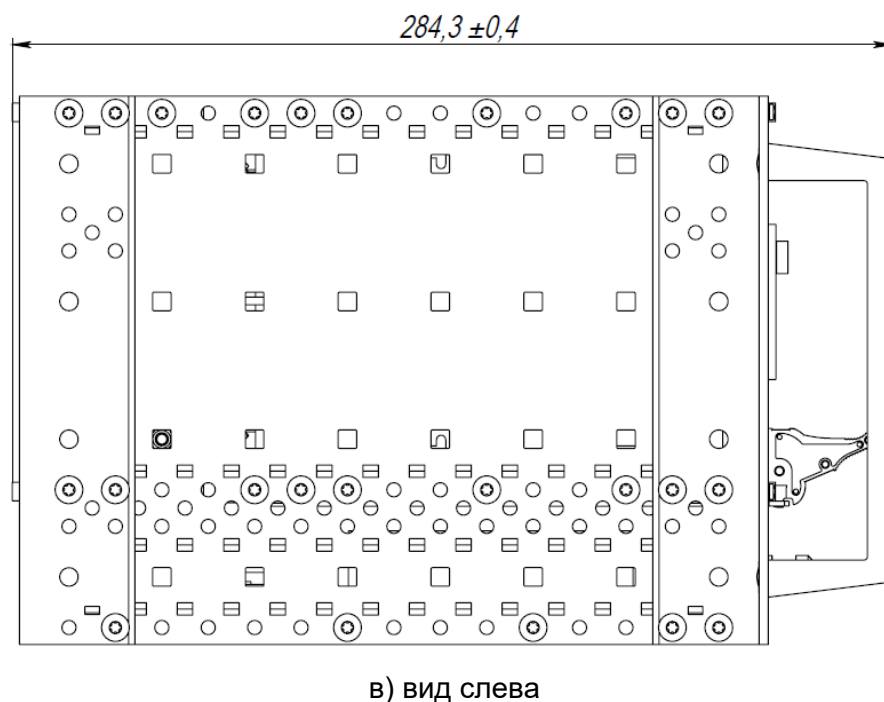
3 Внешний вид и размеры изделия Монтажный каркас 19"/2
